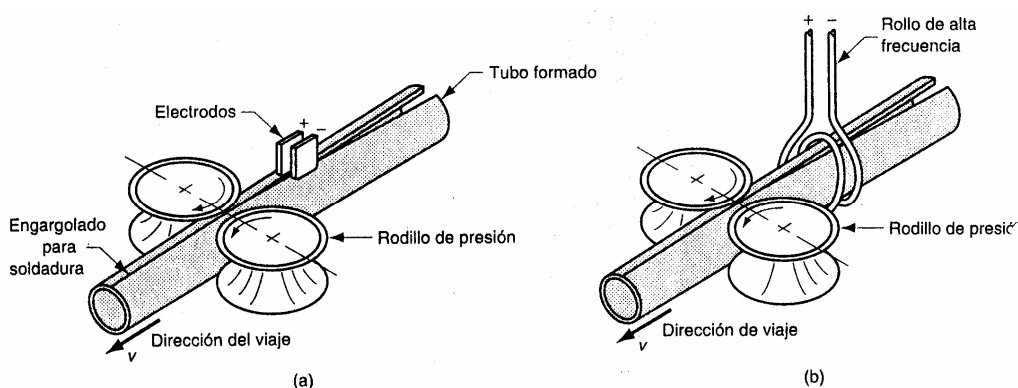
Soldadura de engargolados de tubos mediante (a) Soldadura por resistencia de alta frecuencia y (b) soldadura por inducción de alta frecuencia.
